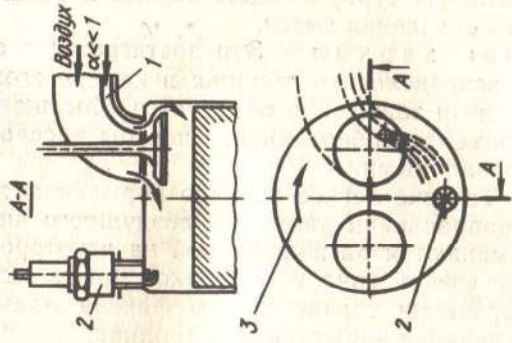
Схема двигателя Будри: 1 — трубопровод богатой смеси; 2 — свеча зажигания; 3 — направление движения вихря
